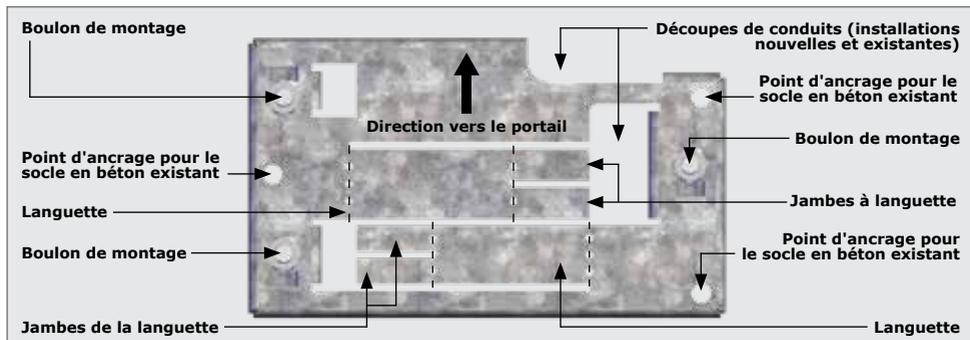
ASSEMBLAGE DE LA PLAQUE DE FONDATION - VUE DE DESSUS
